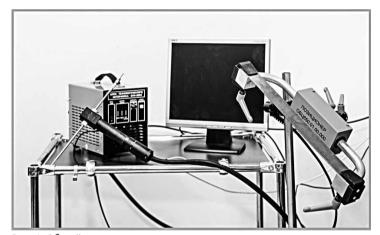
Общий вид малоамперного тренажера сварщика для электродуговой сварки MДTC-05 M1
